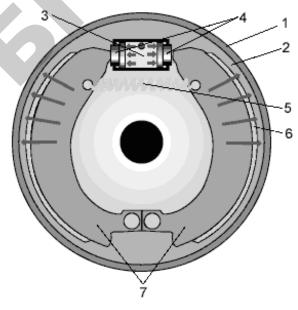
Схема работы барабанного тормозного механизма: I — тормозной барабан; 2 — тормозной щит; 3 — рабочий тормозной цилиндр; 4 — поршни рабочего тормозного цилиндра; 5 — стяжная пружина; 6 — фрикционные накладки; 7 — тормозные колодки
